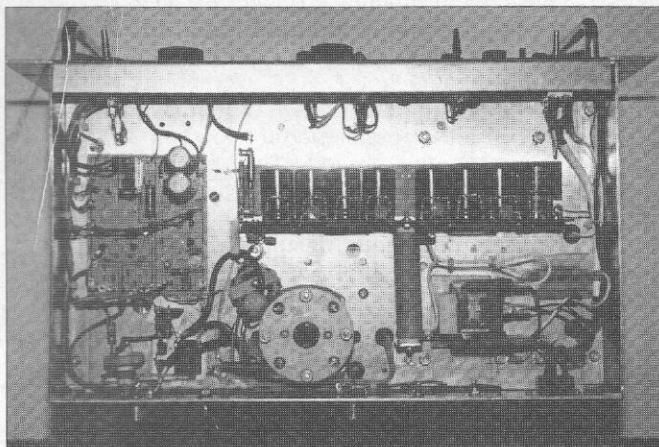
Disposición de los componentes en la parte inferior del chasis. Sobre el módulo de control se han agrupado el mayor número posible de componentes pequeños.
